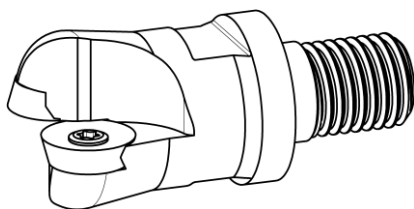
Концевая фреза с резьбовым хвостовиком
